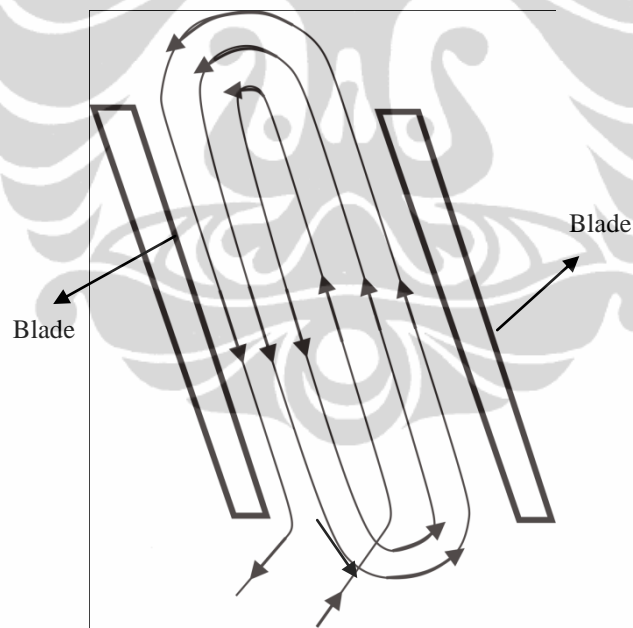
kemungkinan interference antara cutting tool dengan workpiece pada proses roughing impeller diameter 27 mm
